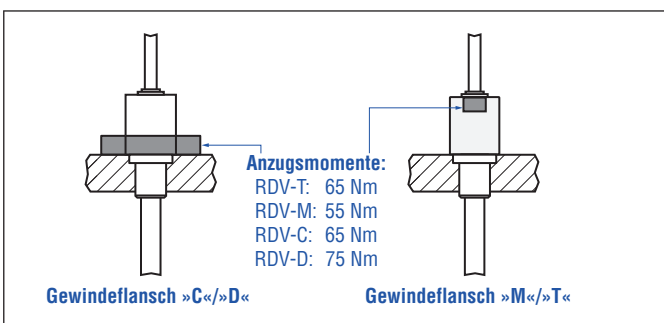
Einbaubeispiel für Gewindeflansch »C«/»D«, »M«/»T«
